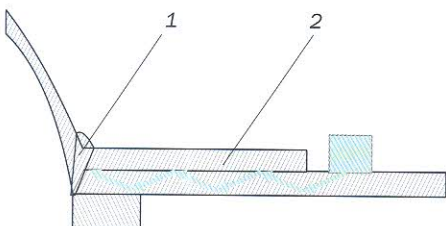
АУЗК внутреннего сварного соединения «патрубок–обечайка»: 1 – внутреннее сварное соединение «патрубок–обечайка», 2 – накладка на патрубок
